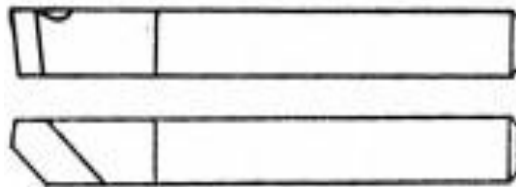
Резец 2100– 0556 ГОСТ 18869– 73.
